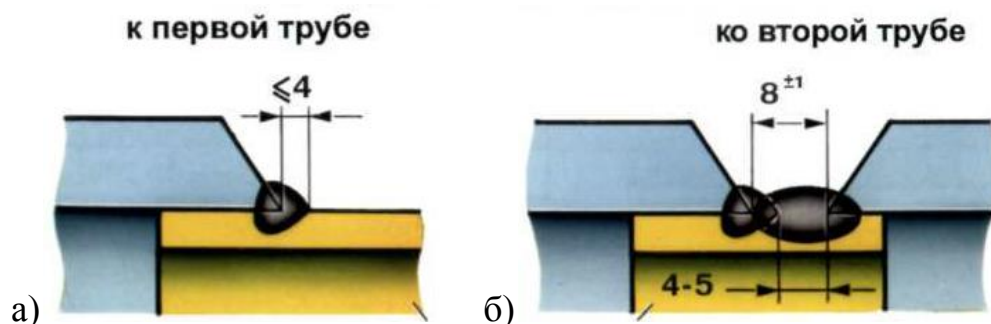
Приварка подкладного кольца к первой (а) и второй (б) трубам
